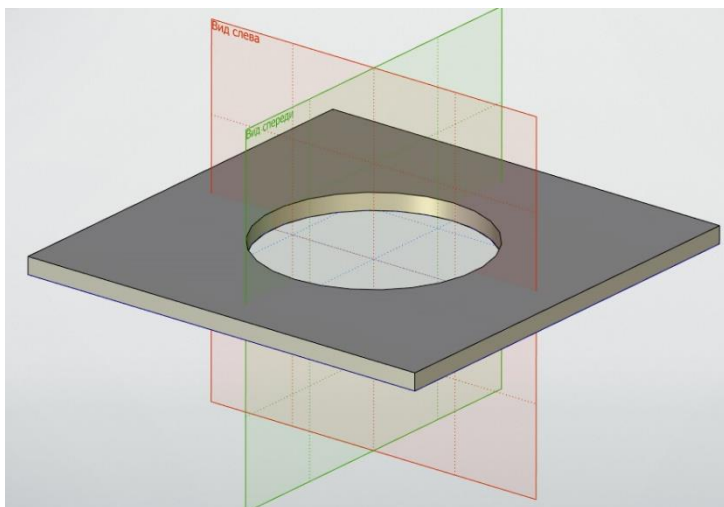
Нижняя часть верхней пластины опорно-поворотного устройства
